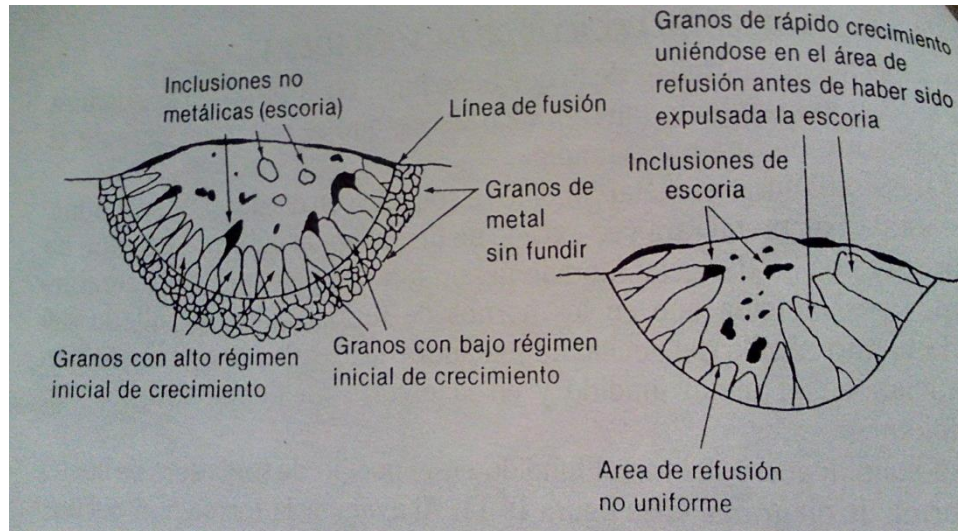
Solidificación en soldadura y tipos de grano en la ZAT
